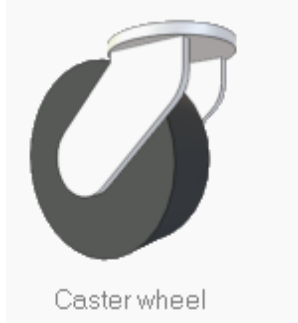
Модель подруливающего колеса «Caster wheel»
